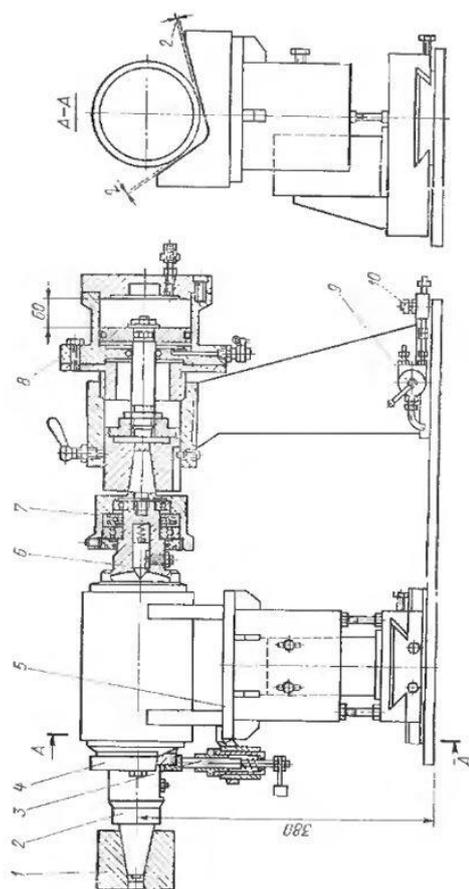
Приспособление для автоматической сварки кольцевых швов воздушного баллона трактора Т-150:
